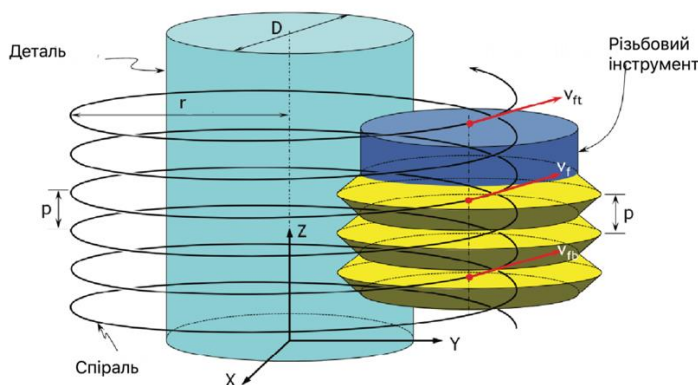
Відносне розташування різьбонарізного інструменту до заготовки при фрезеруванні різьби
